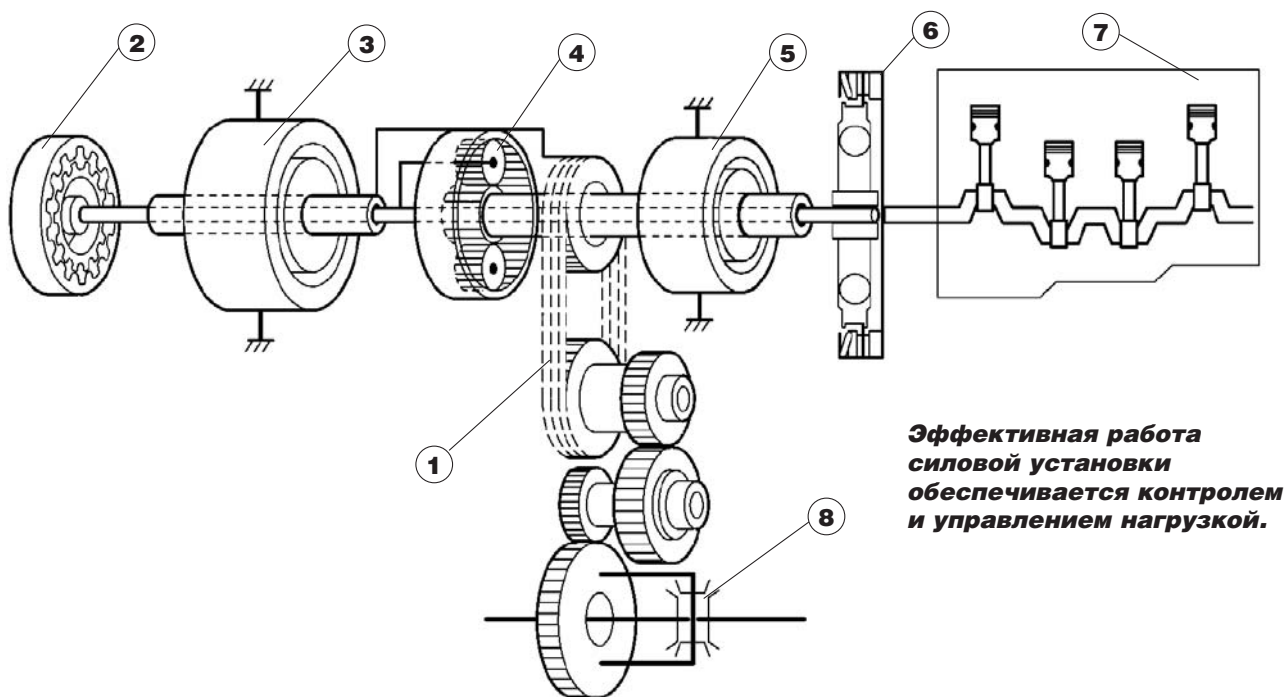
Схема гибридной установки Toyota Prius. Момент идет на колеса через планетарную передачу, объединяющую основные агрегаты. Бензиновый двигатель связан с водилом, электромотор - с коронной шестерней, а генератор - с солнечной: 1 - бесшумная приводная цепь; 2 - масляный насос; 3 - электромотор; 4 - планетарная передача; 5 - генератор; 6 - трансмиссионный демпфер; 7 - бензиновый двигатель; 8 - дифференциал.
